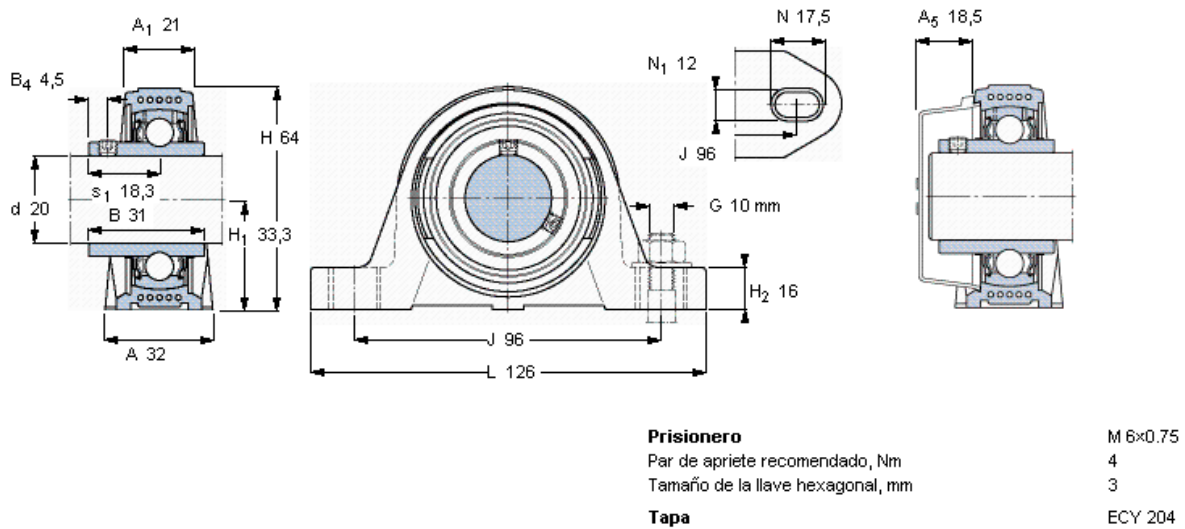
Representación y dimensiones del soporte Y-TECH. Fuente. SKF.
